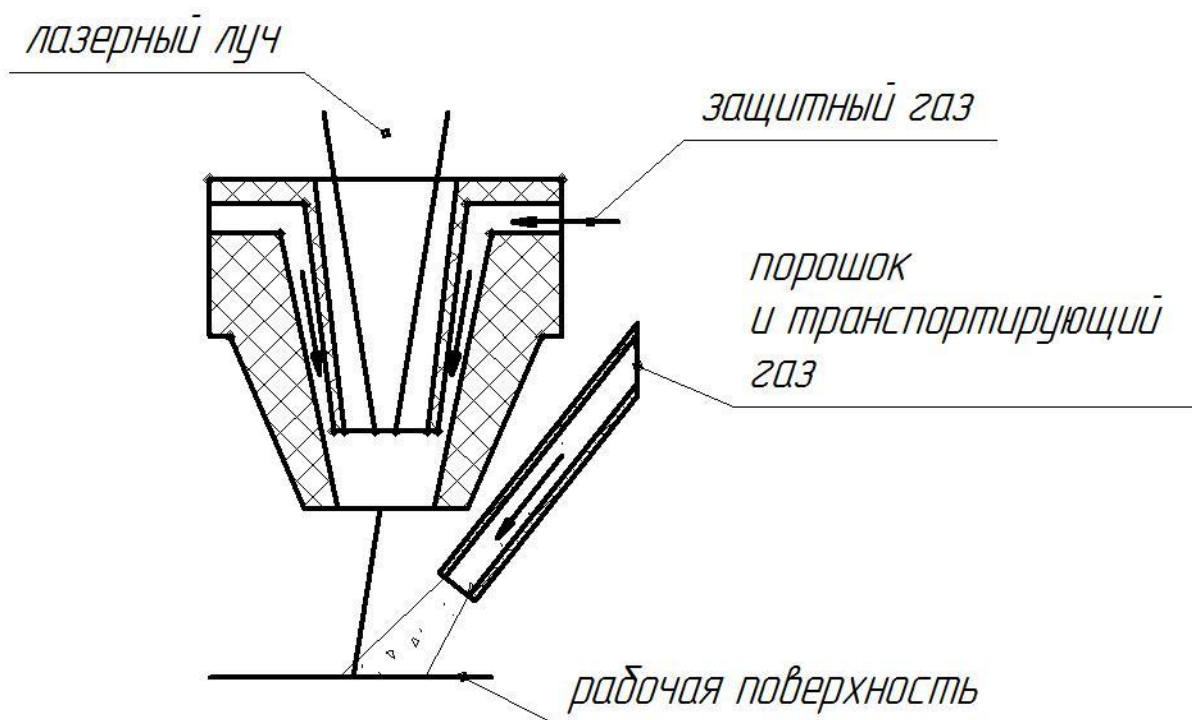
Схема лазерной наплавки с боковой подачей порошка
